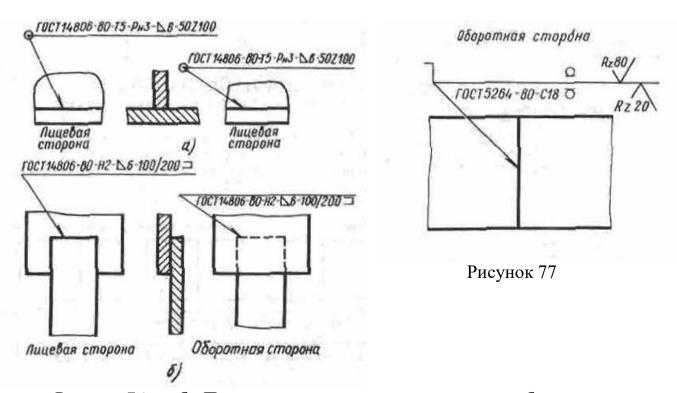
а, б - Приведены сварные швы с условными обозначениями На рисунках 76 - 77 приведены сварные швы с условными обозначениями, которые расшифровываются с учётом, того ГОСТ 2.312 — 72 допускает не указывать способ сварки. На этих чертежах в качестве примера дано условное изображение шва как на лицевой стороне, так и на его обратной стороне.
